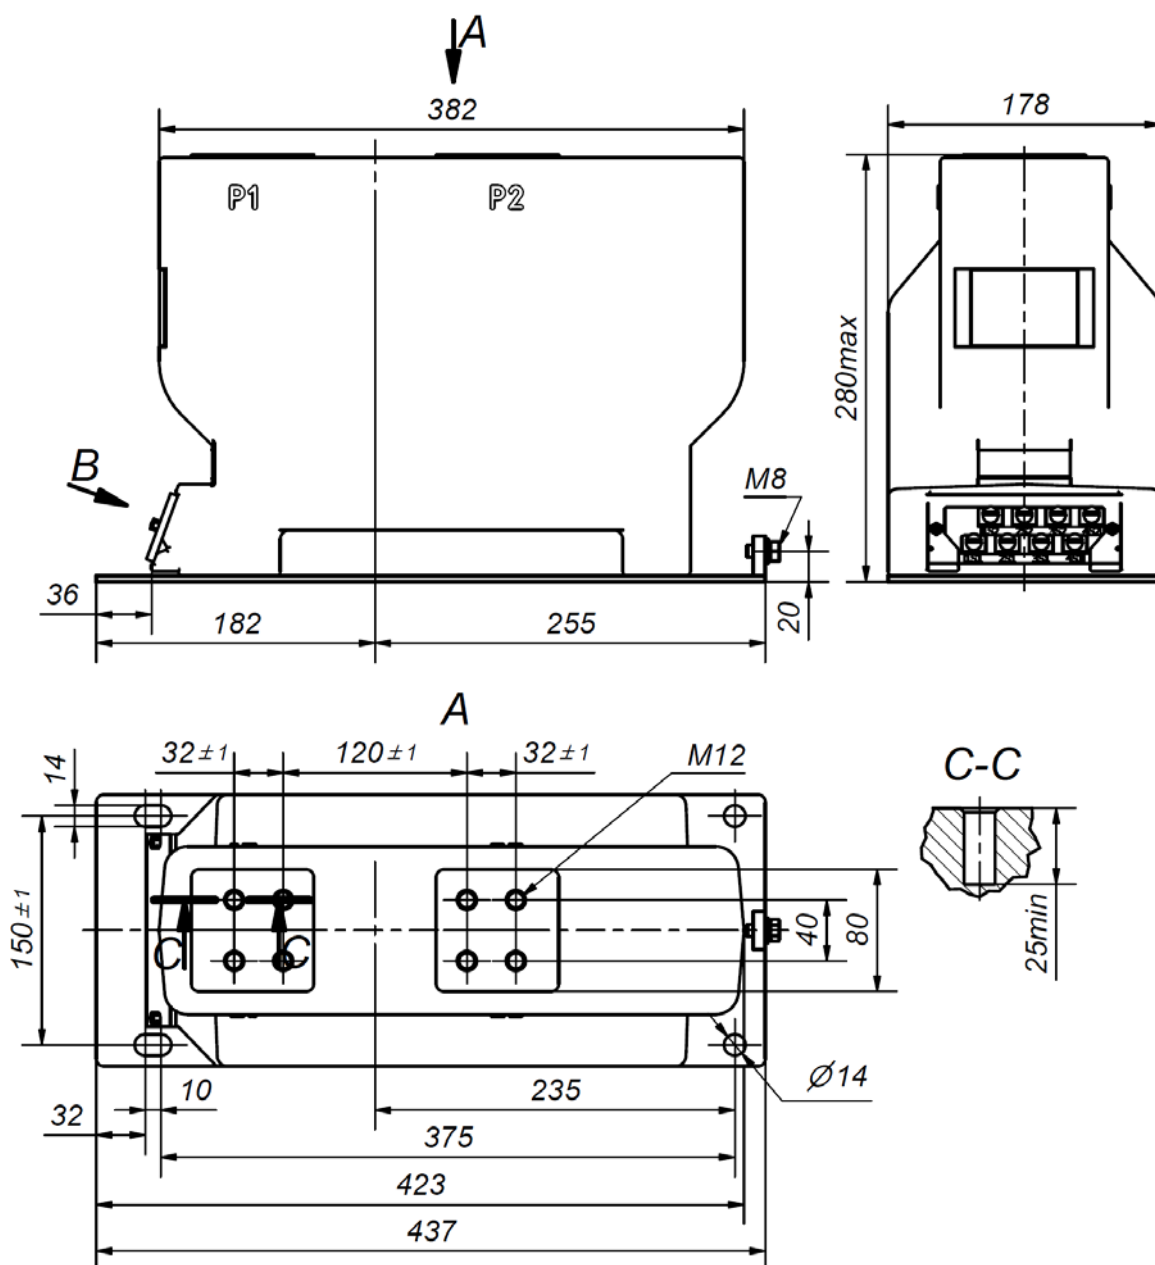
Габаритный чертеж трансформаторов TCS1-12-23.XX.2...
